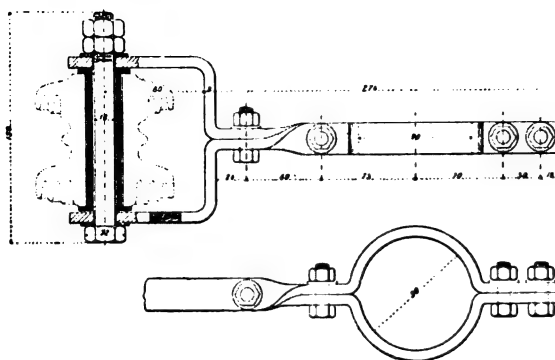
et 17. — Chape pour fixer sur poteau un isolateur d'arrêt.
